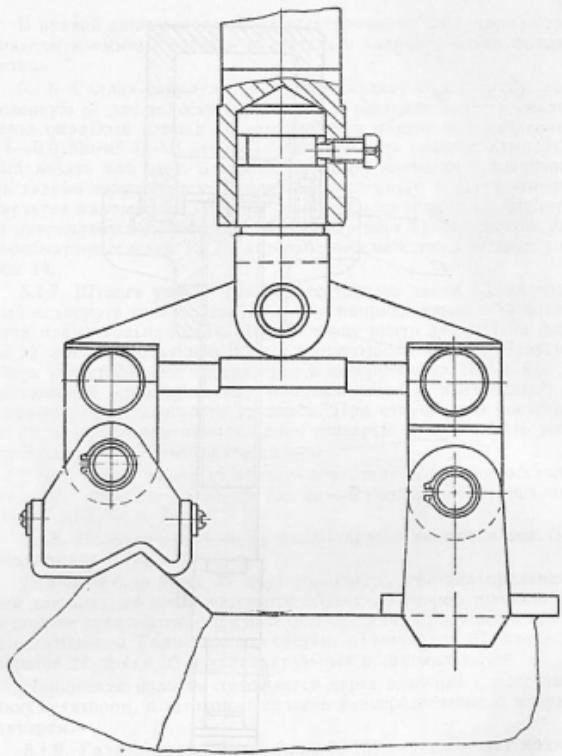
Упор съёмочный пяточной для обуви 265..305размеров.
